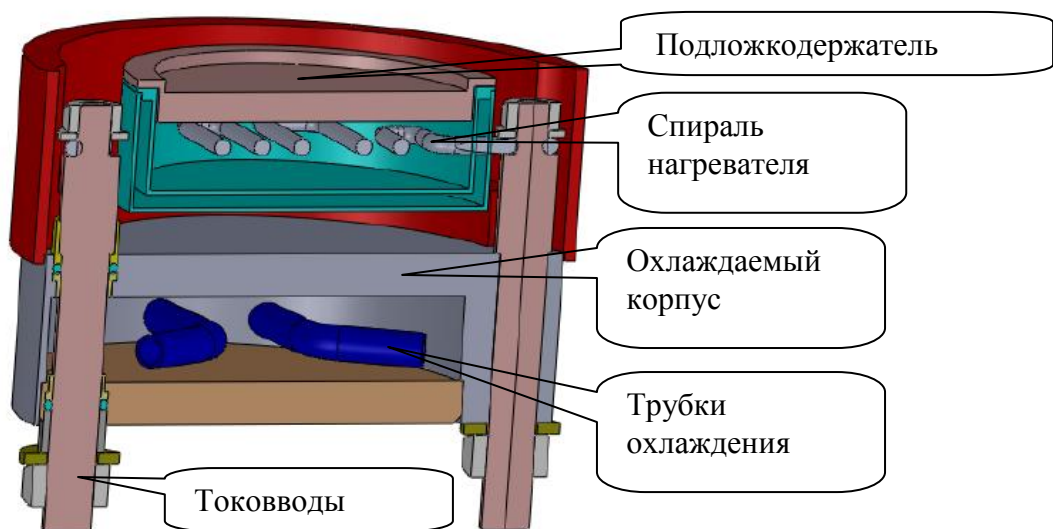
Конструкция нагревателя-подложкодержателя.
